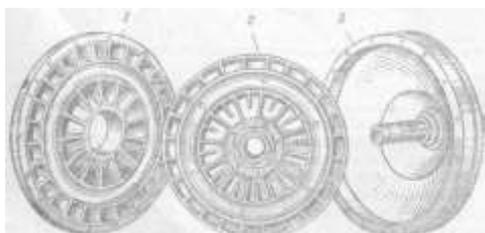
Рабочие органы гидромuфты: 1 — насосное колесо; 2 — турбинное колесо; 3 — вращающийся корпус
